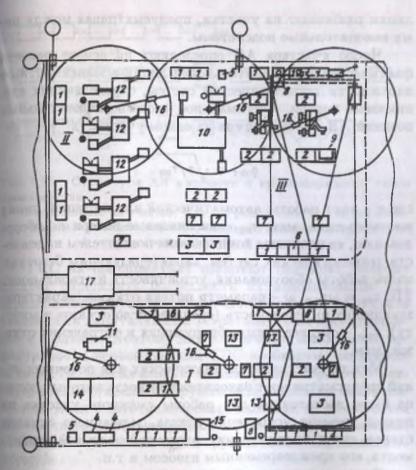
Планировка участка сборки инструментальных магазинов, редукторов и шпиндельных бабок:
